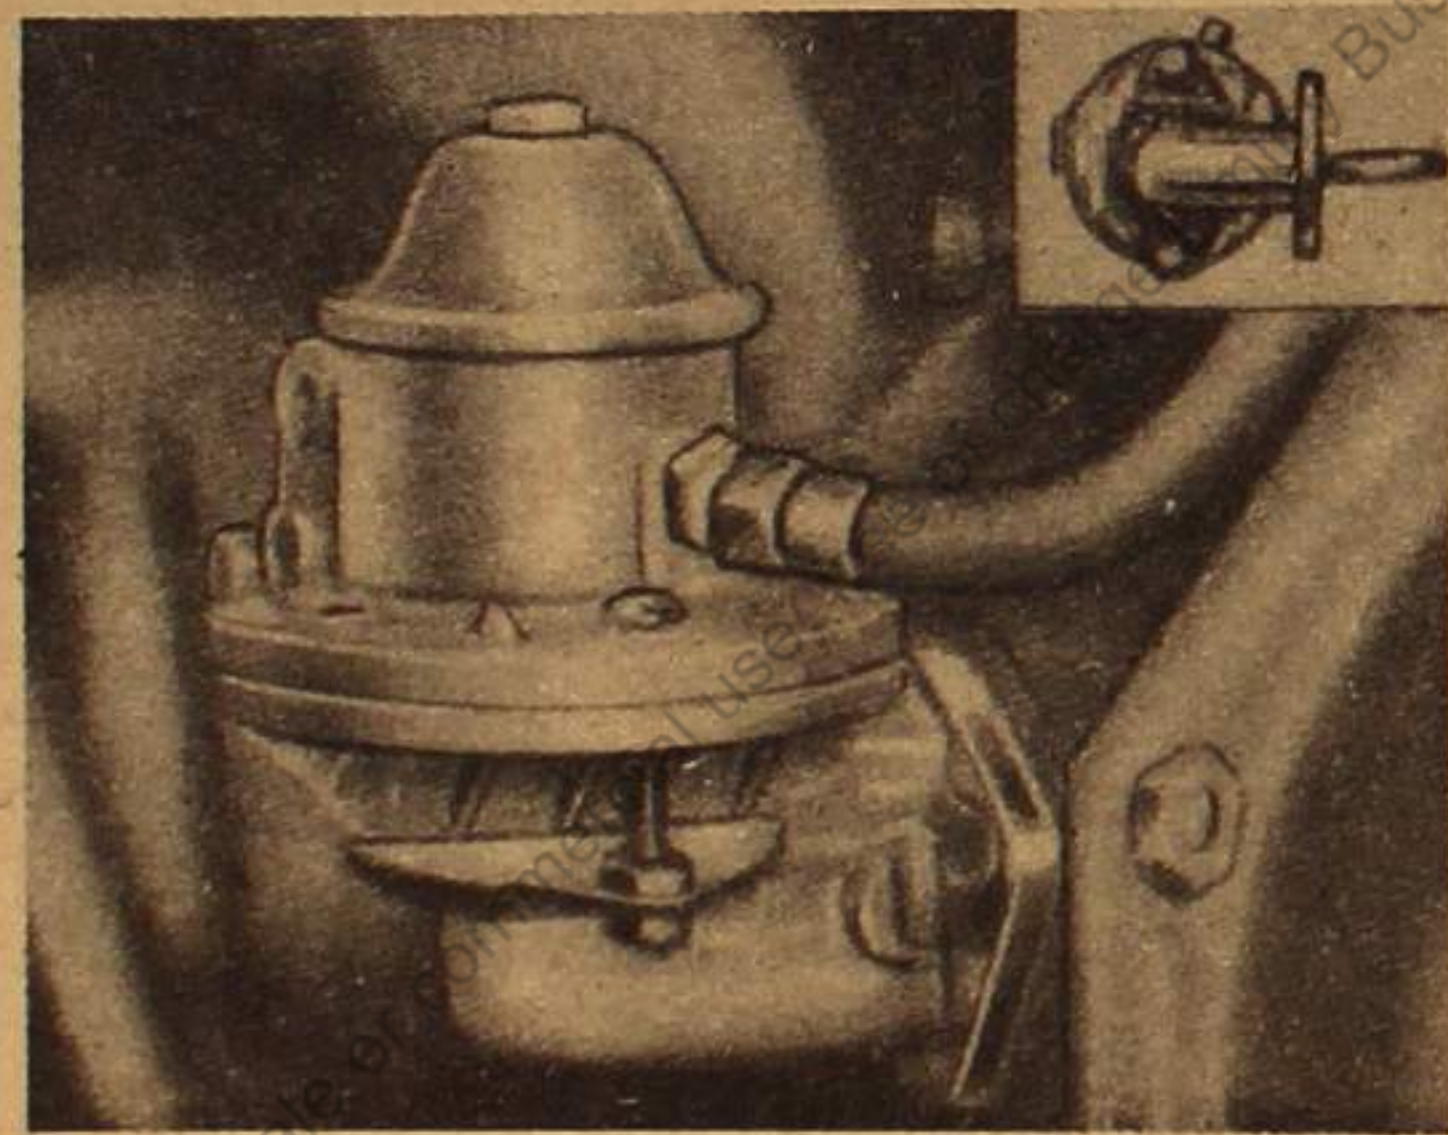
Einstellbohrungen im Kraftstoffpumpen-Gehäuseunterteil durch einen mit Filz ausgefüllten Halter abgedichtet.
